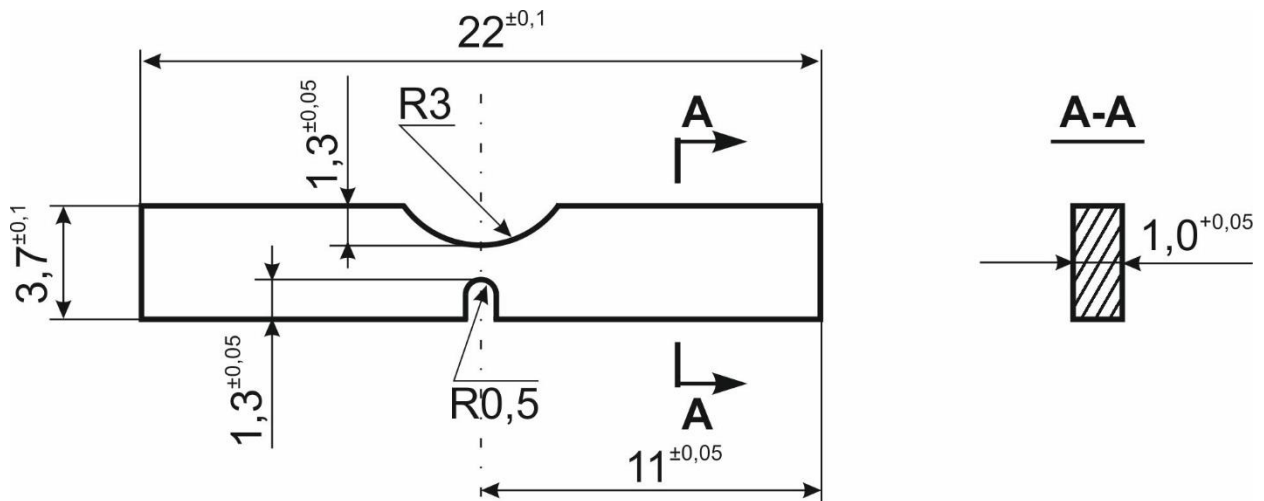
Образец для испытаний на ударный изгиб, изготовленный из половинки стандартного образца Шарпи
